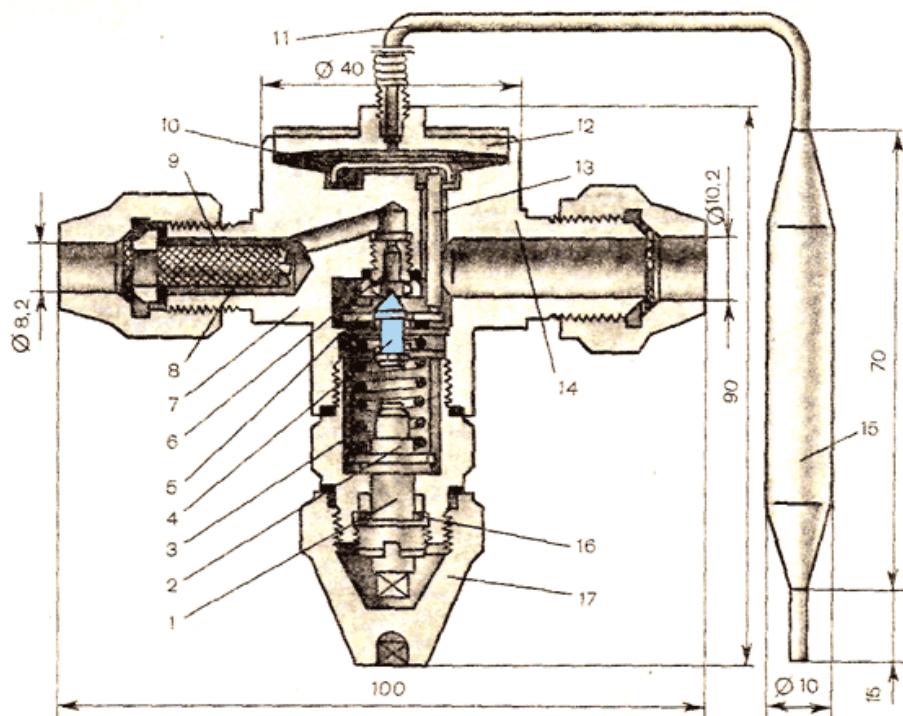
Приклад конструктивного виконання ТРВ: 1 – гвинт регулювання перегріву; 2 – шток; 3 – пружина; 4 – клапан; 5 – напрямна; 6 – сідло клапана; 7 – корпус; 8 штуцер усмоктувального трубопровода; 9 – фільтр; 10 – мембрана; 11 - капілярна трубка; 12-корпус мембрани; 13-вирівнювальна трубка; 14 - вихідний штуцер; 15-термобалончик приладу; 16-сальник; 17- захистна кришка.
